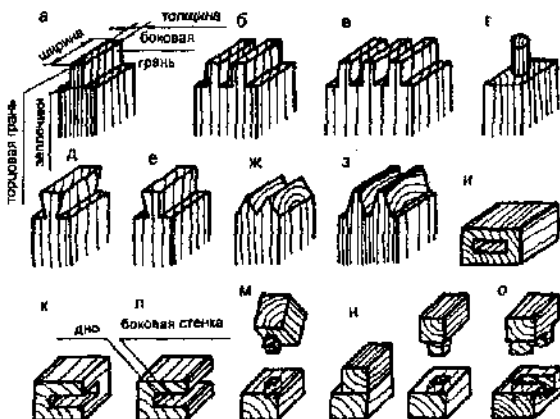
Виды шипов: а — одинарный; б — двойной; в — многократный; г — круглый; д — «ласточкин хвост»; е — односторонний «ласточкин хвост»; ж, з — зубчатые; и — гнездо; к, л — проушины; м — глухой шип; н — шип впотемок; о — шип в полупотемок
